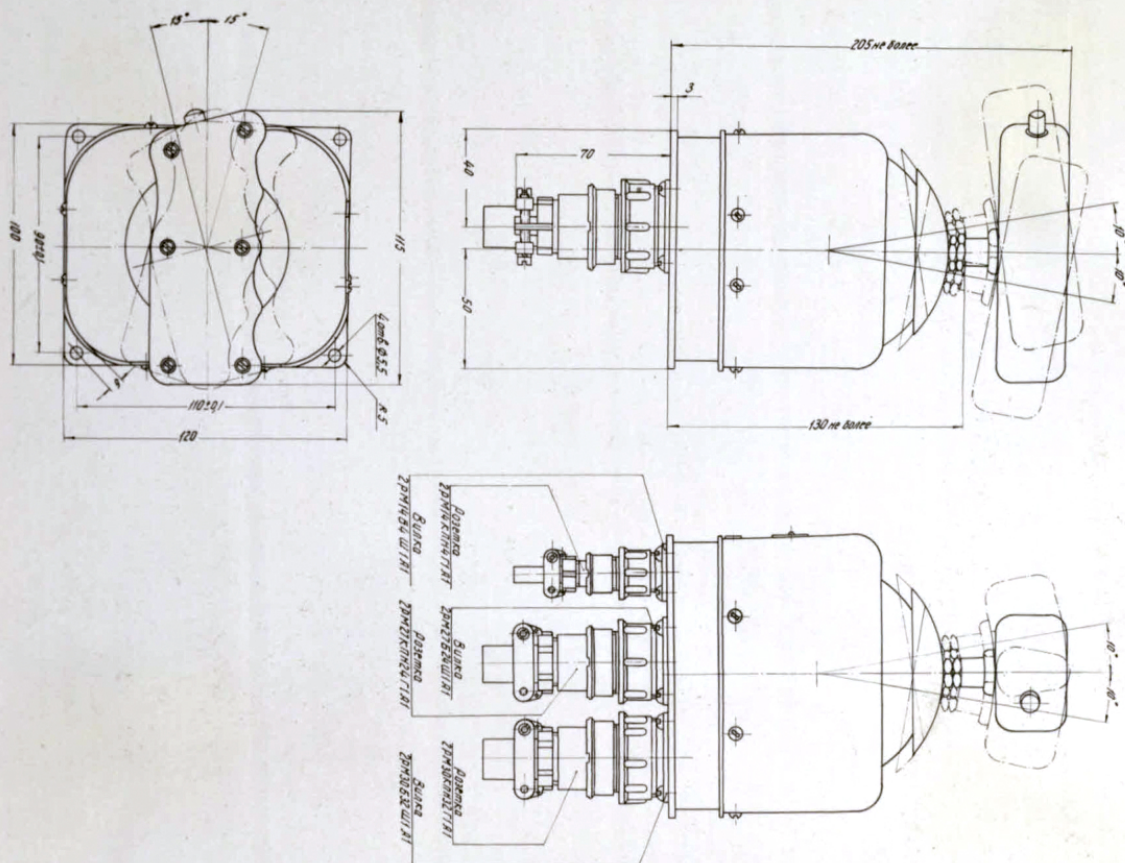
Габаритный чертёж ручки управления РУ1Б
